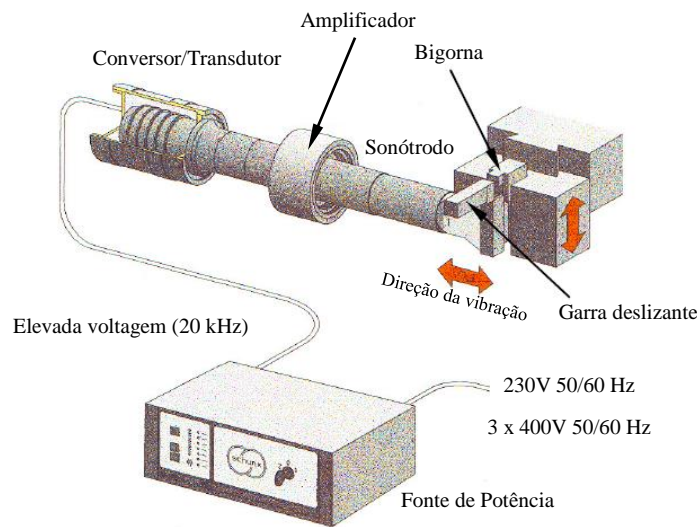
Equipamento de Soldadura por Ultrassons (adaptado de [45]).
